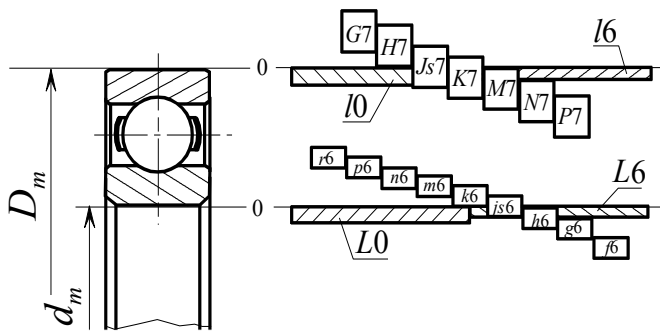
Схема расположения рекомендуемых полей допусков посадочных размеров для подшипников классов точности 0 и 6
